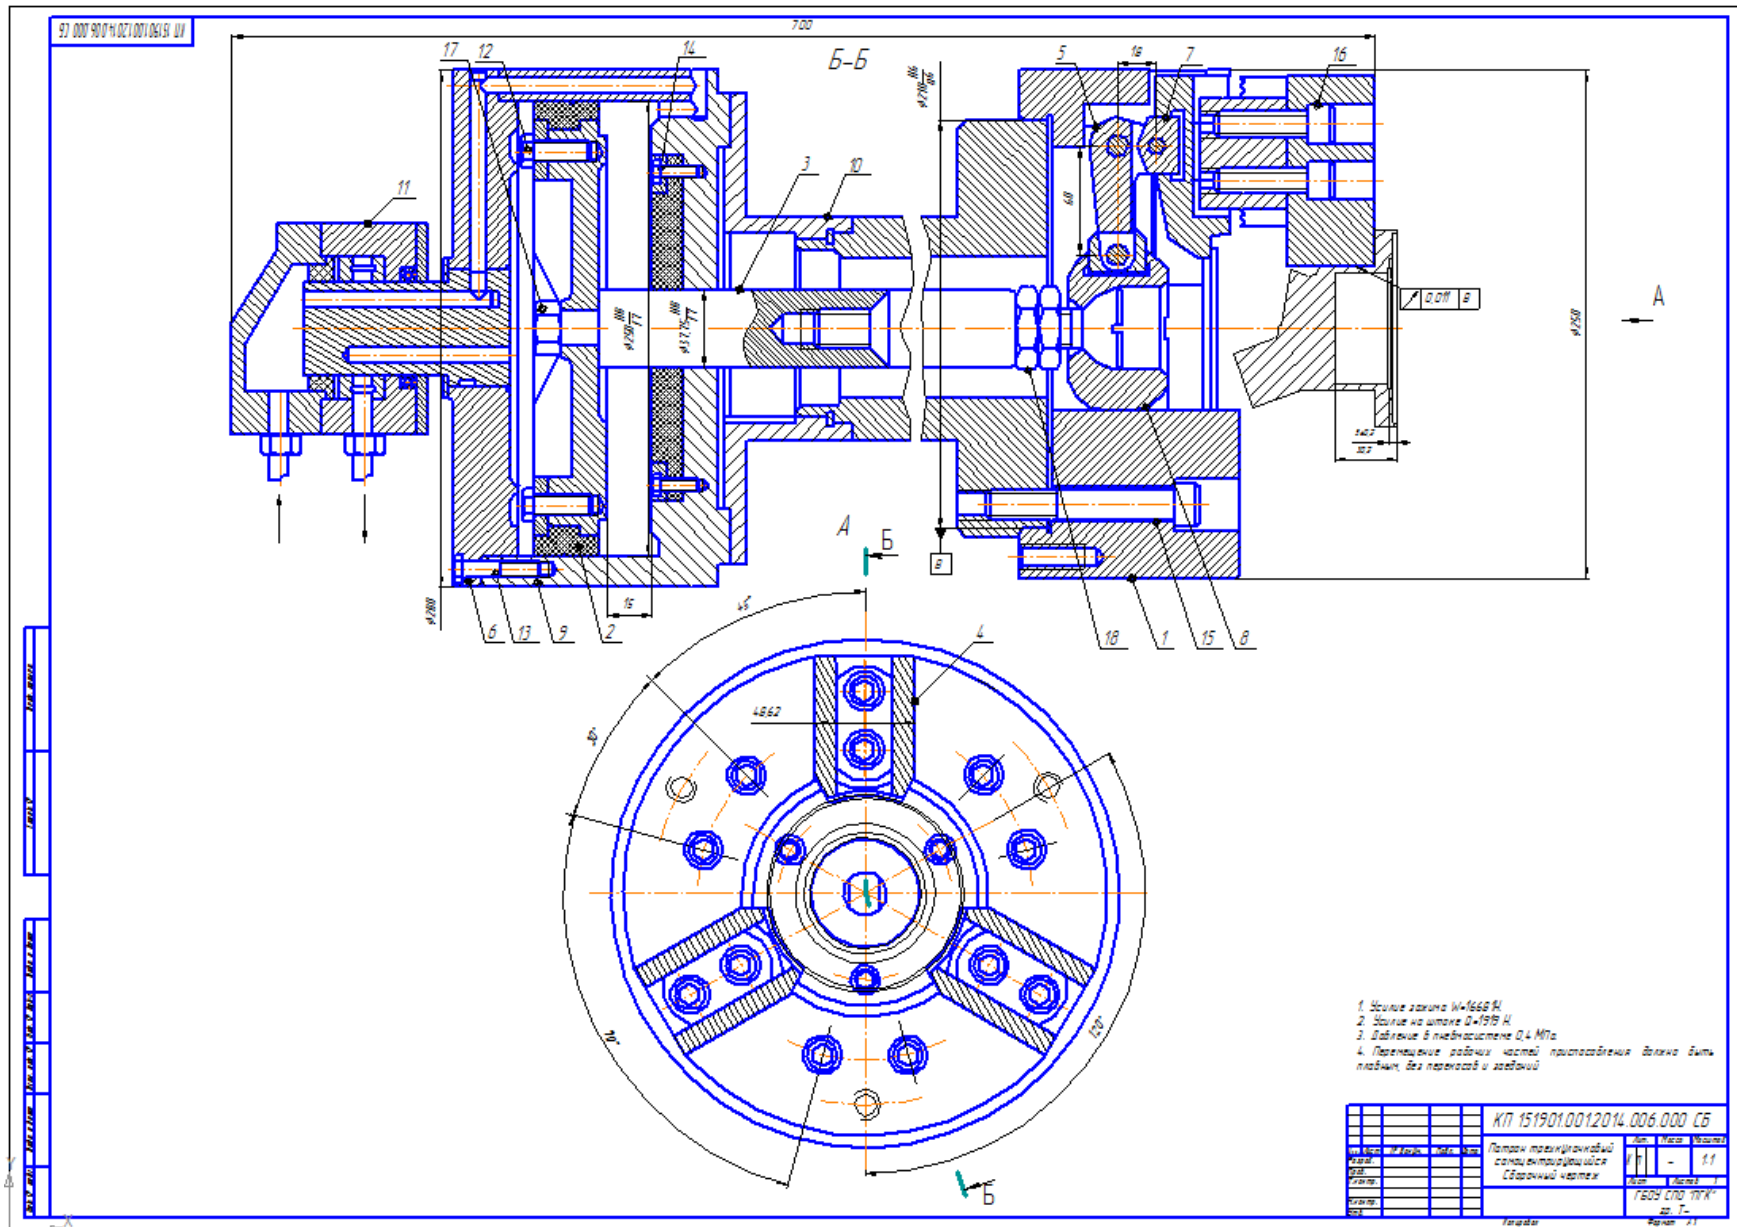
Патрон трехкулачковый самоцентрирующийся (сборочный чертеж).
